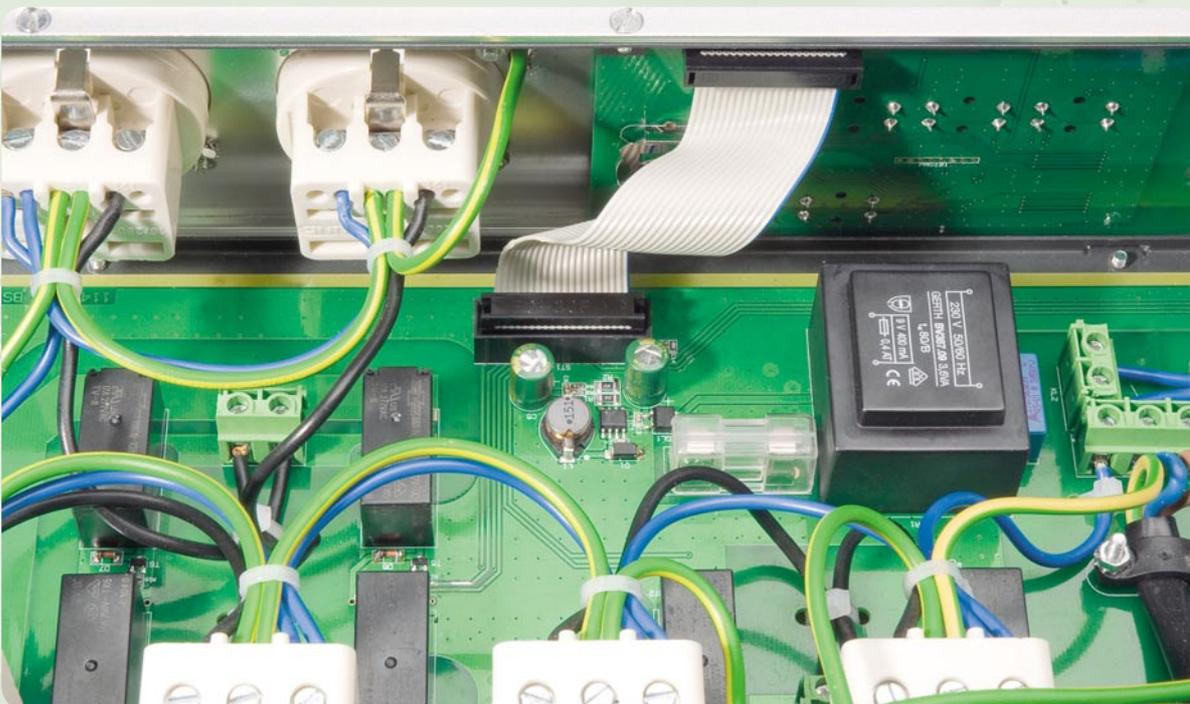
Montage der Einzelladern an die Steckdosen des Frontprofils und Fixierung der Leiter mit Kabelbindern mit Blick auf die Frontseite
